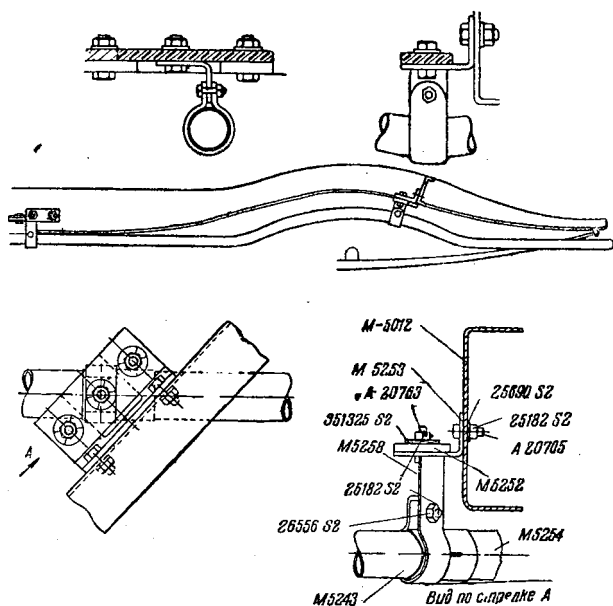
Схема подвески глушителя и выхлопной трубы М-1.
